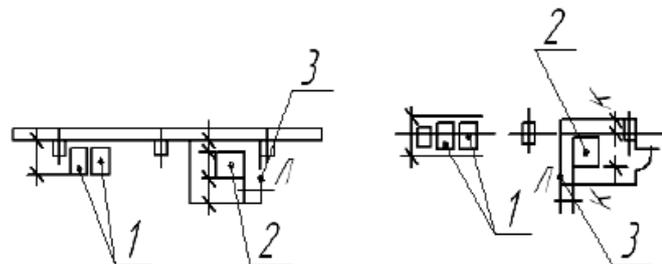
Размещение оборудования для сварки длинномерных деталей:
